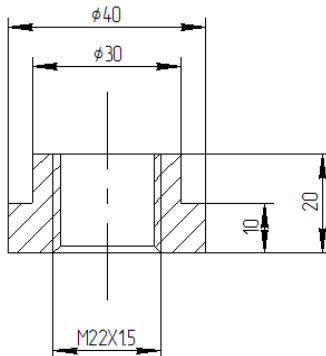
Габаритные и присоединительные размеры патрубка дренажа
